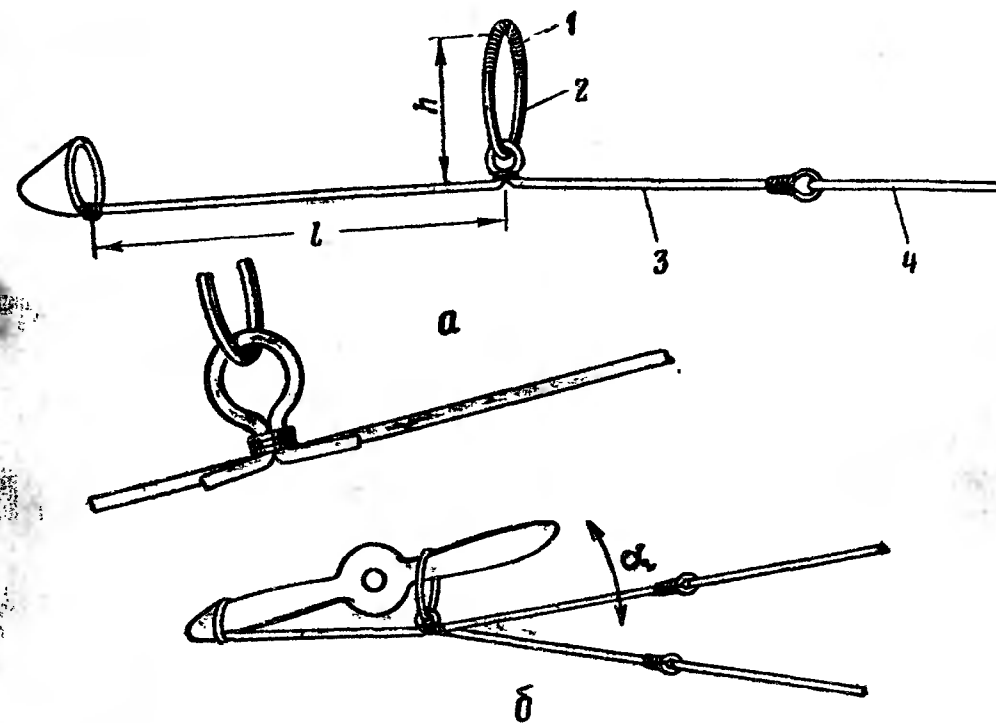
Приспособление для безопасного пуска двигателя с помощью резинового амортизационного шнура: 1 — войлочная обшивка; 2 — веревочная петля; 3 — амортизационный резиново-тканевый шнур; 4 — трос, а — деталь крепления петли; б — схема надевания приспособления на винт.
